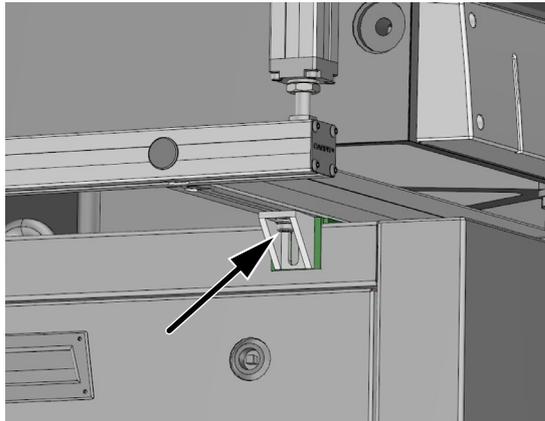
Winkel anschrauben Profil (Abbildung beispielhaft)
